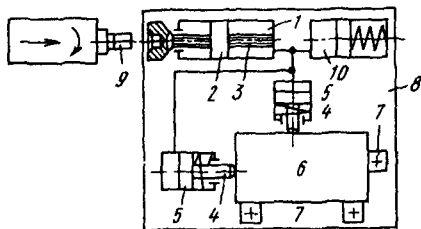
Схема закрепления заготовки на спутнике с помощью гидравлических приватов
